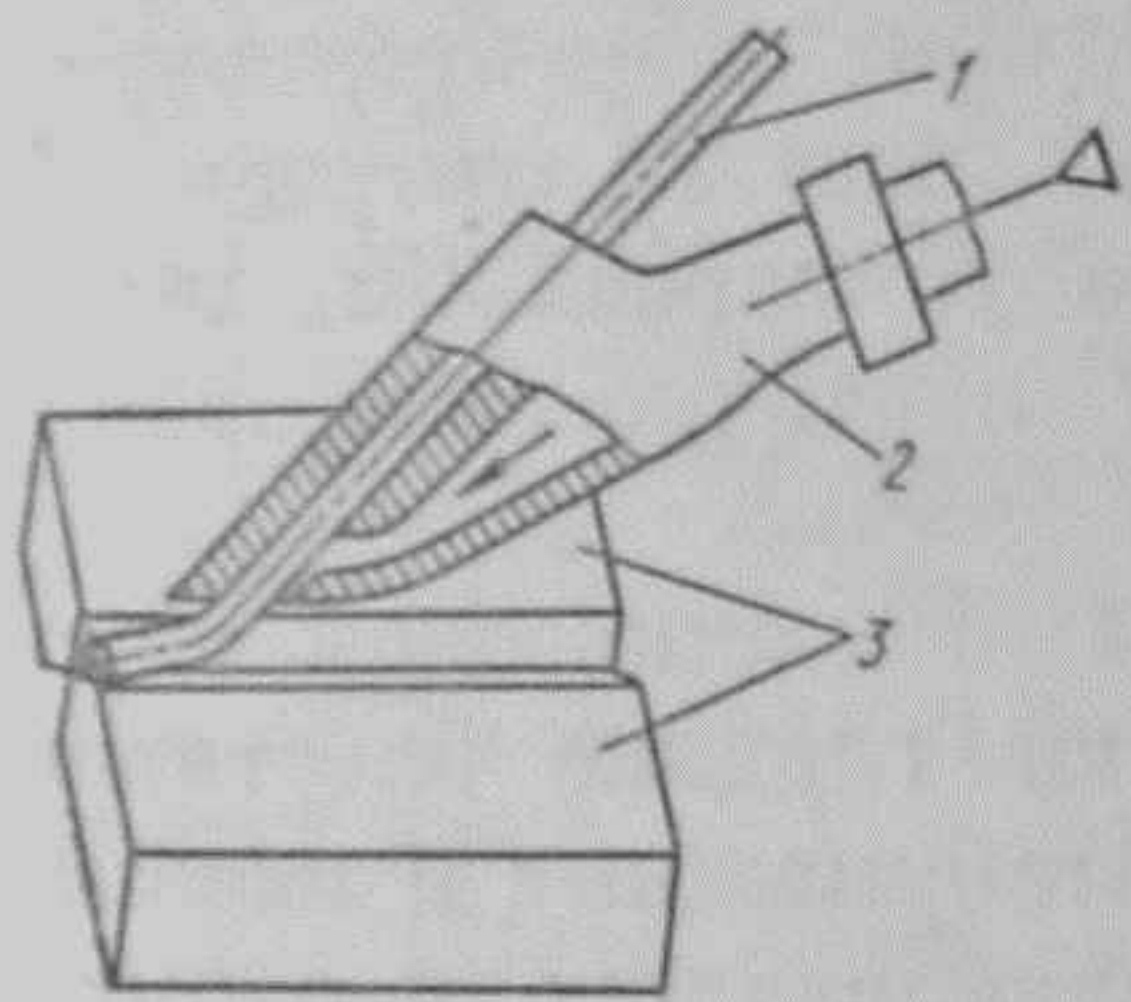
Схема сварки нагретым газом с использованием присадочного прутка
